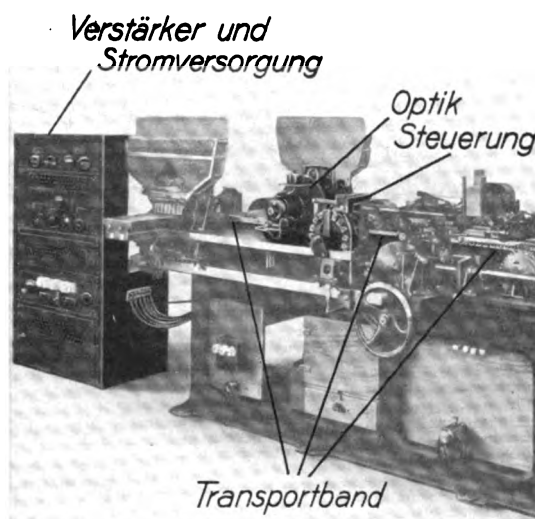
Zigarettenpackmaschine mit lichtelektrisch gesteuerter Spiegelgeleeinrichtung.
